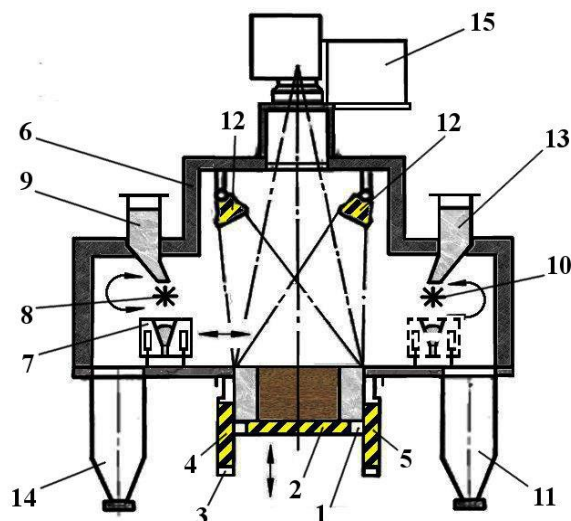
Схематическое изображение СЛС для изготовления деталей из полиэфиркетона: 1 - платформа, 2 - нагреватель, 3 - сменная рама, 4 и 5 - нагреватели, 6 - рабочая камера, 7 - двойной нож, 8 - шлицевой вал, 9 - дозатор, 10 - шлицевой вал, 11 - бункер сбора порошка, 12 - верхние нагреватели, 13 - дозатор, 14 - бункер сбора порошка, 15 - лазерно-сканирующая система
